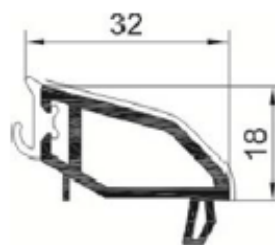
Planșa în secțiune transversală a montantului (Cat. No. 8044.00) profile PVC.
